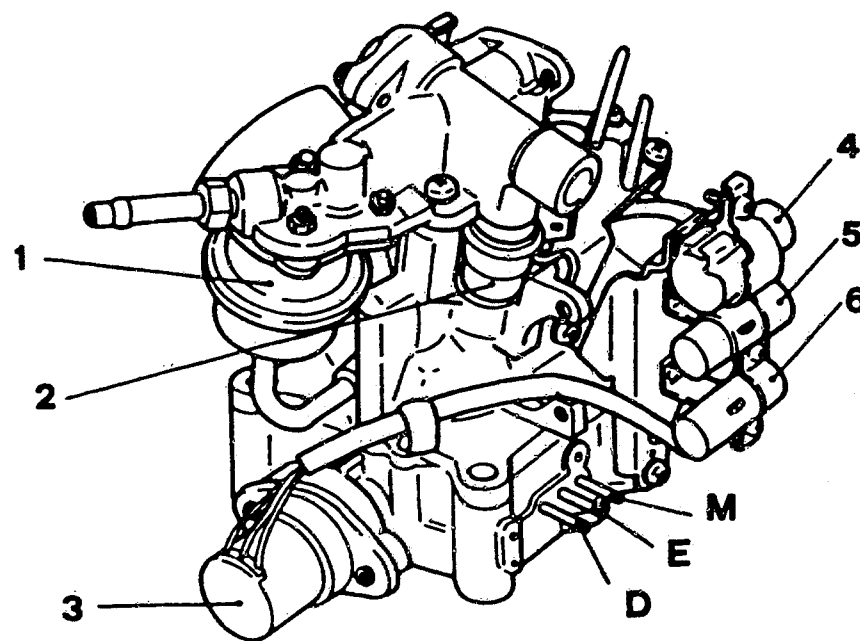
Die komplette Einspritzeinheit mit ihren wichtigsten Teilen: 1 Kraftstoffregler – 2 Einspritzventil – 3 Drosselklappenschalter (TPS) – 4 Stecker des Motorpositionssensors – 5 Stecker des Leerlaufdrehzahlreglers – 6 Stecker des Drosselklappenschalters – D, E, M = Unterdruckanschlüsse
